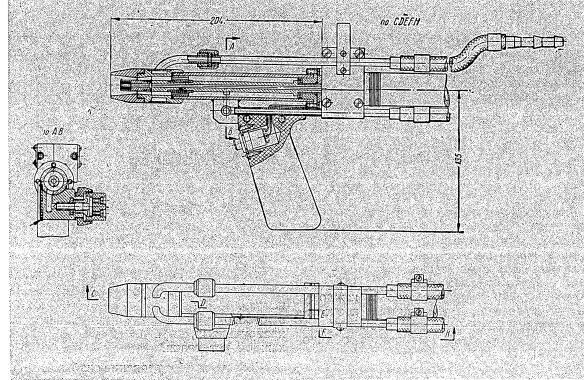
Сварочная головка полуавтомата ПДША-500
